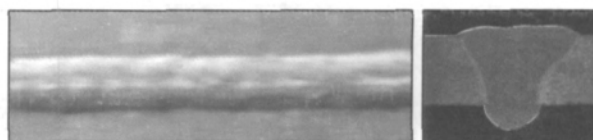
激光填丝焊接焊缝外观及截面形貌
